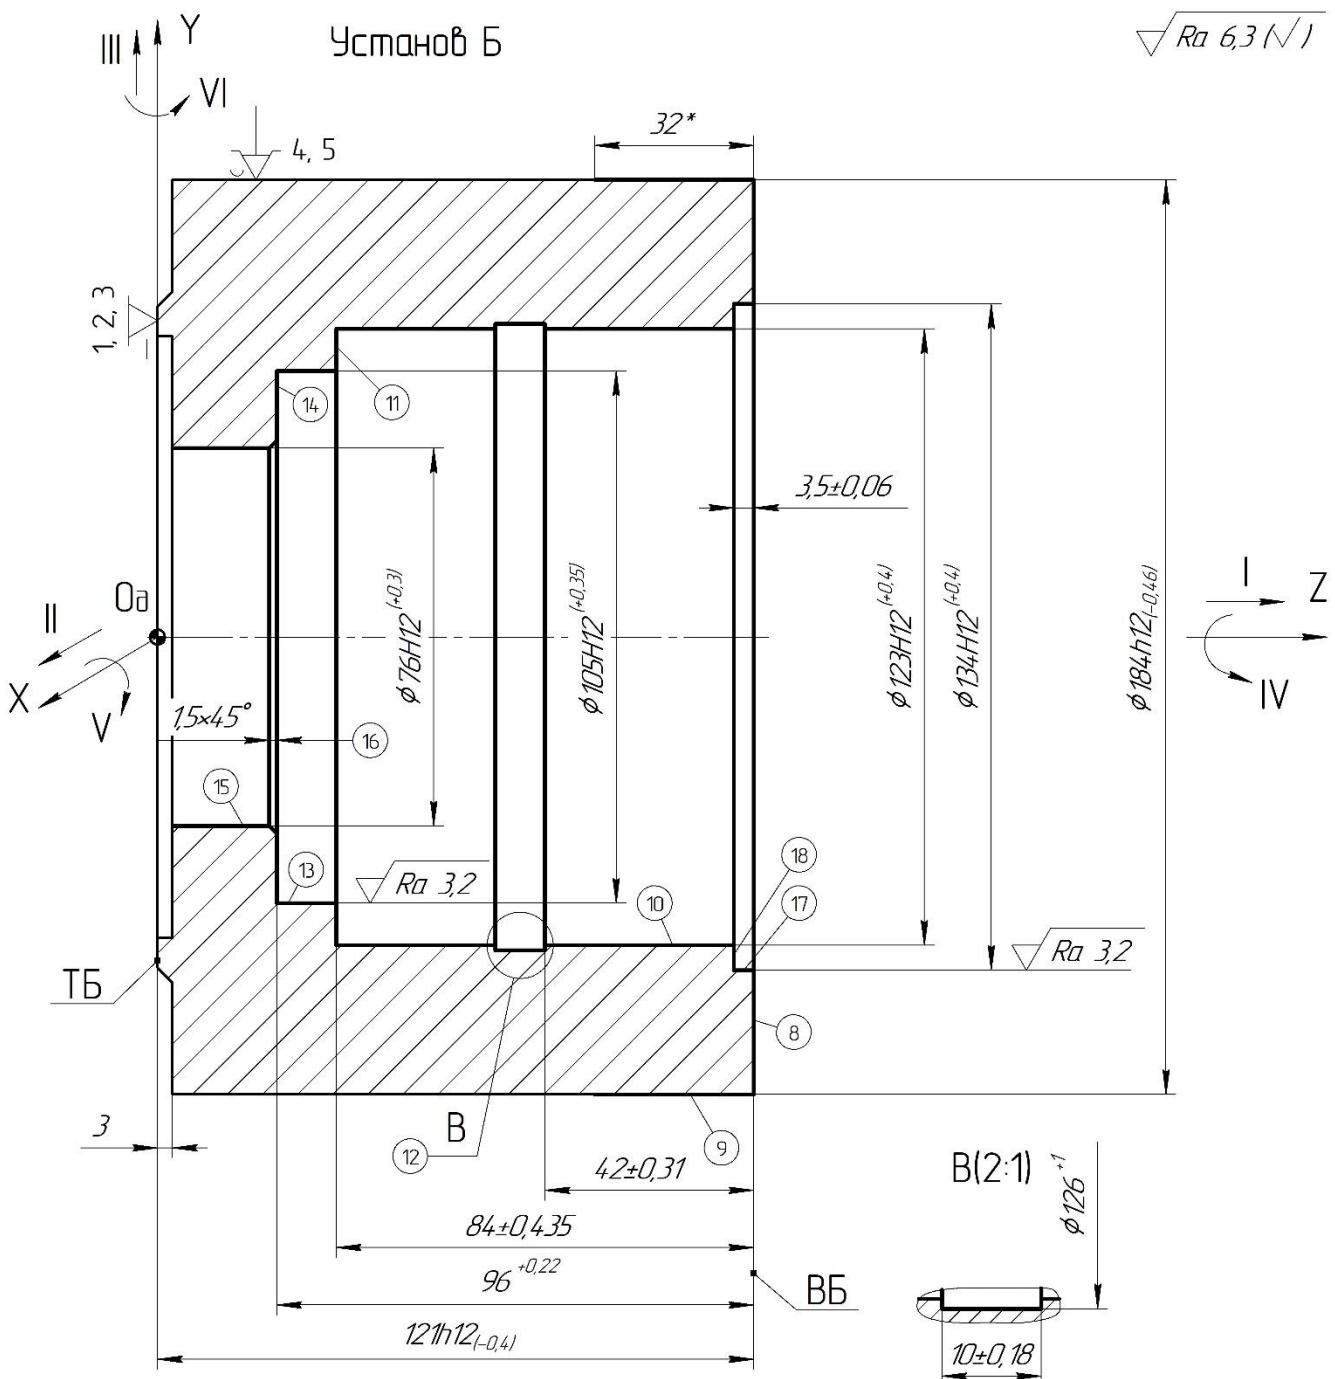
Схема установки заготовки на операції 015 «Токарна з ЧПК».
